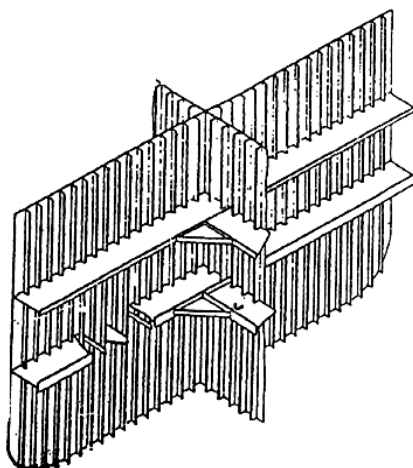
Пересечение поперечной и продольной переборок
